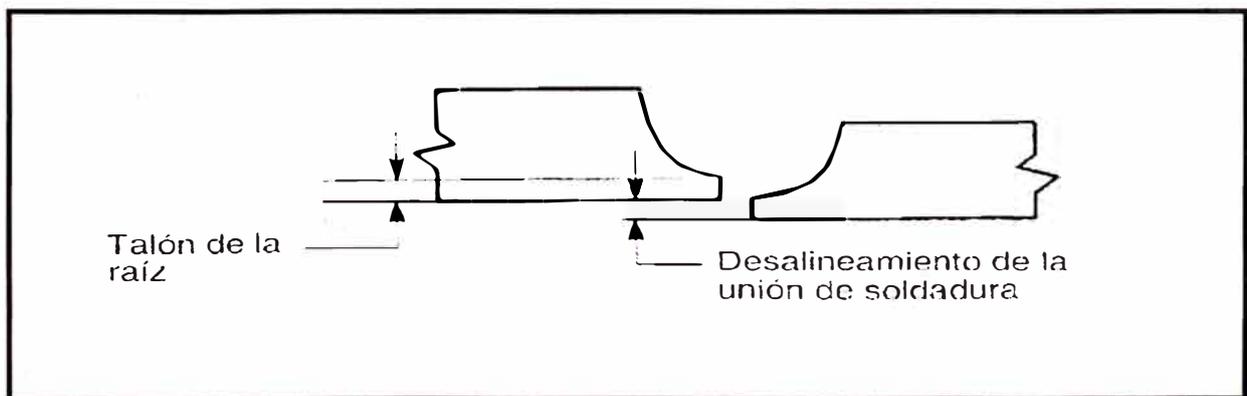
Desalineamiento de la Unión de Soldadura
